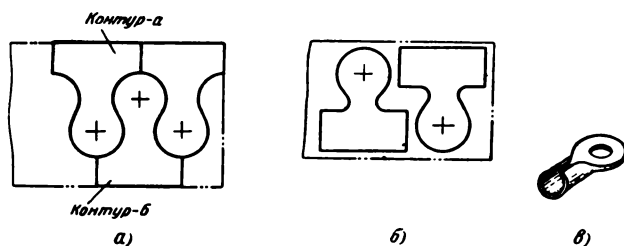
Схемы вырубki заготовки кабельного наконечника.
